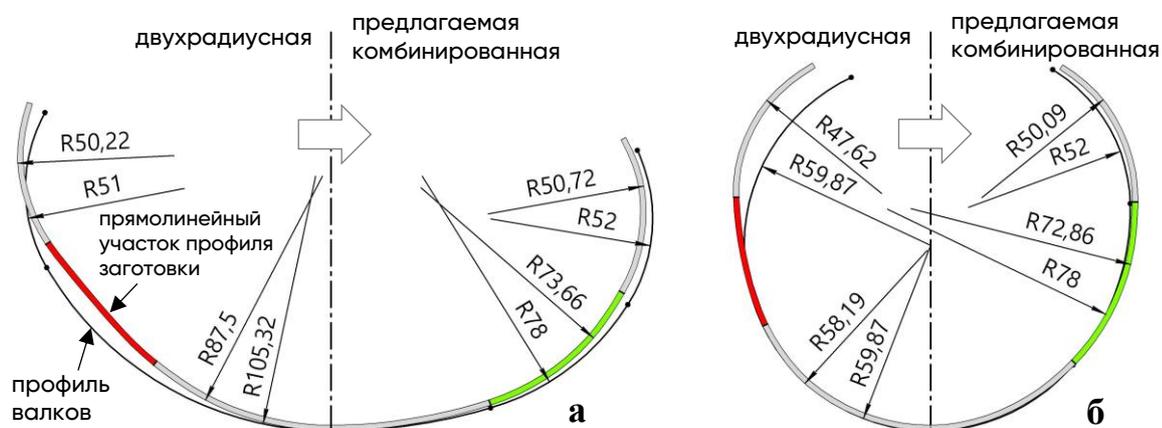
Предлагаемая схема формоизменения трубной заготовки
